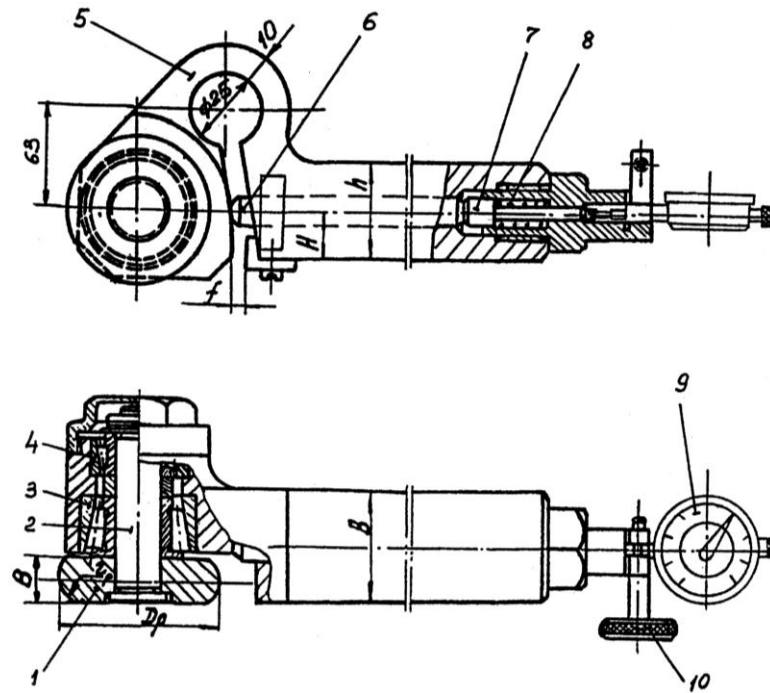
Пристосування з пружинячим корпусом і індикаторним вимірюванням зусилля обкачування:
